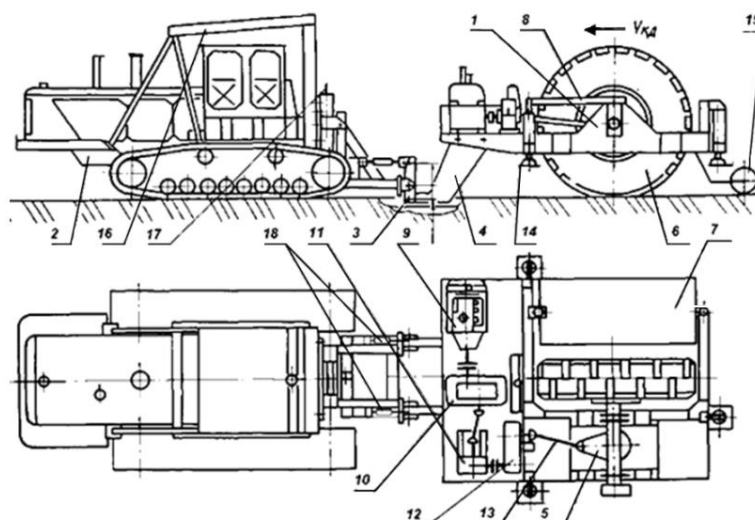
Стенд для испытания одиночного колесного движителя с крупногабаритной шиной
